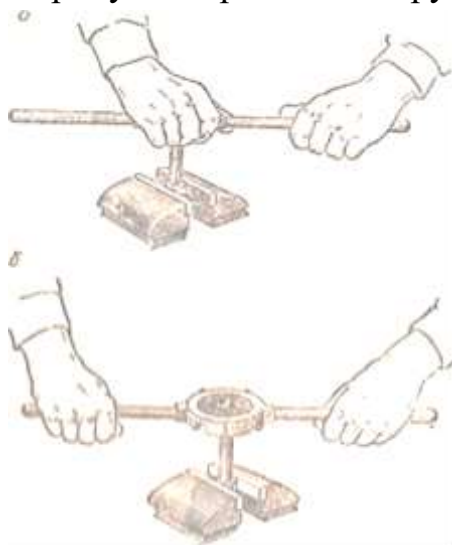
Нарезание резьбы круглыми плашками
